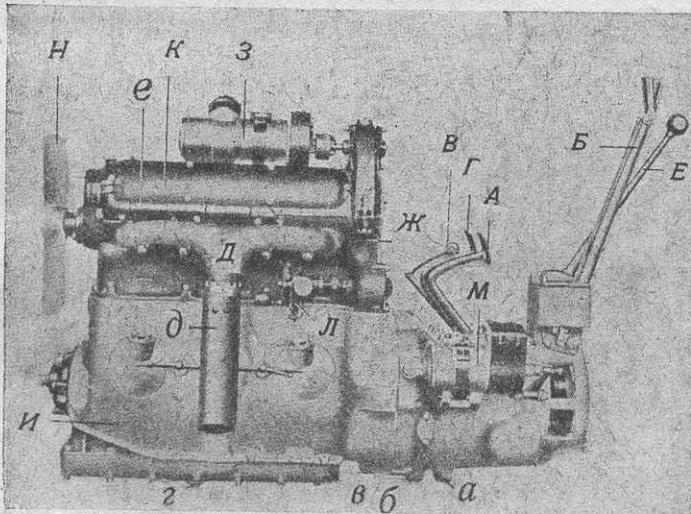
Шестицилиндровый двигатель Штейр 15/70 л. с. (вид со стороны выхлопа).
